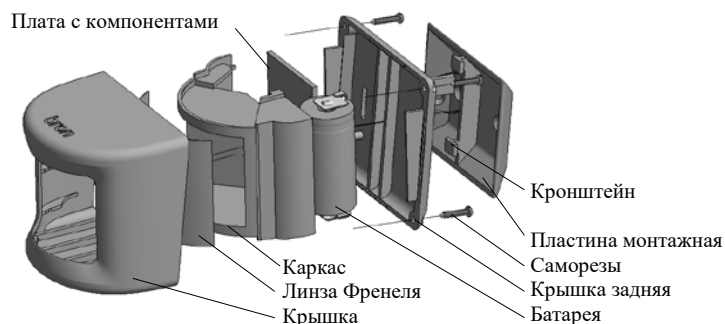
Вид внутренней конструкции (крышка снята)
